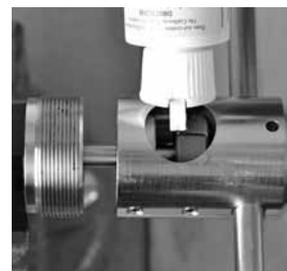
Application d'huile de coupe par l'ouverture prévue pour les copeaux
